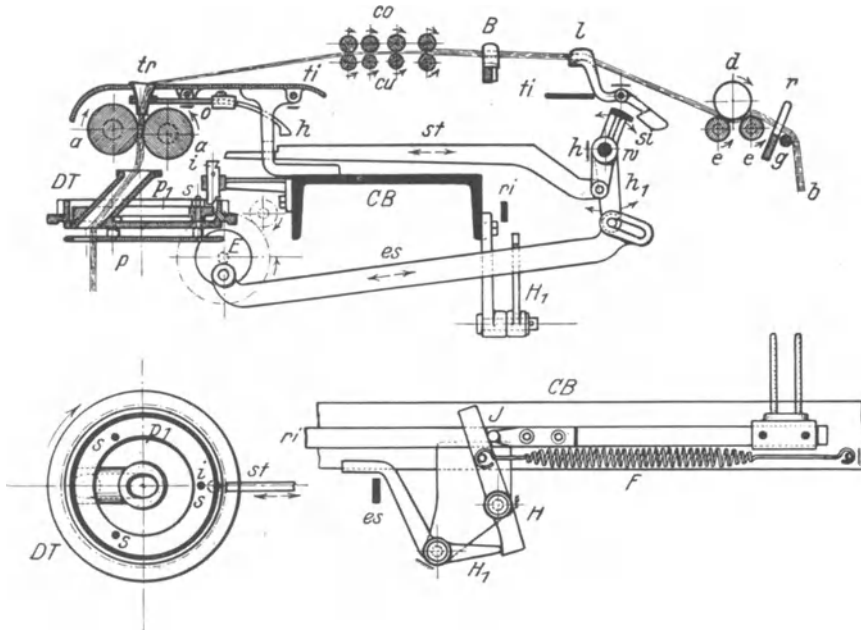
286. Selbsttätige mechanische Ausrückung.
